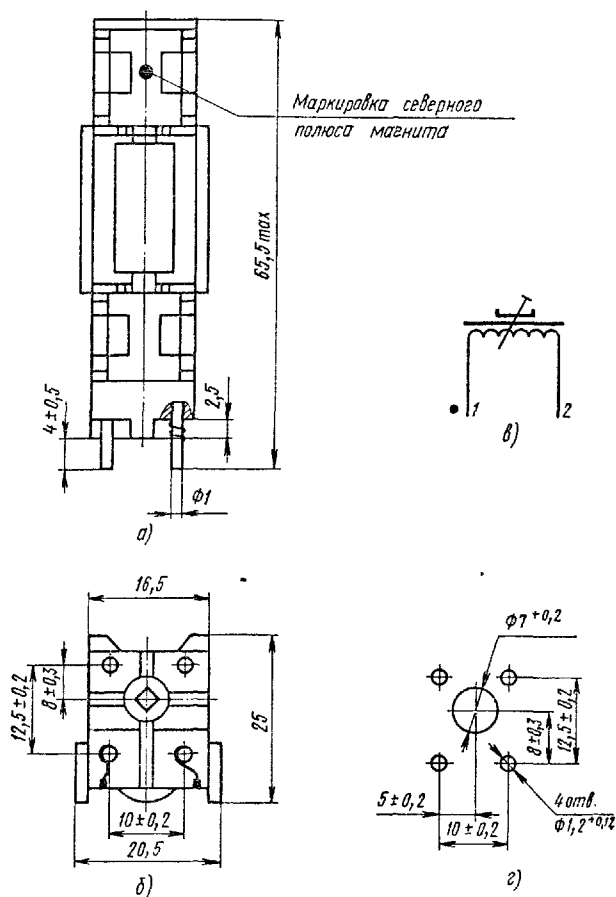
Регуляторы линейности строк РЛС-1, РЛС-2, РЛС-3, РЛС-4 (а, б — габаритный чертеж; в — схема электрическая; г — разметка на печатной плате для крепления РЛС)
